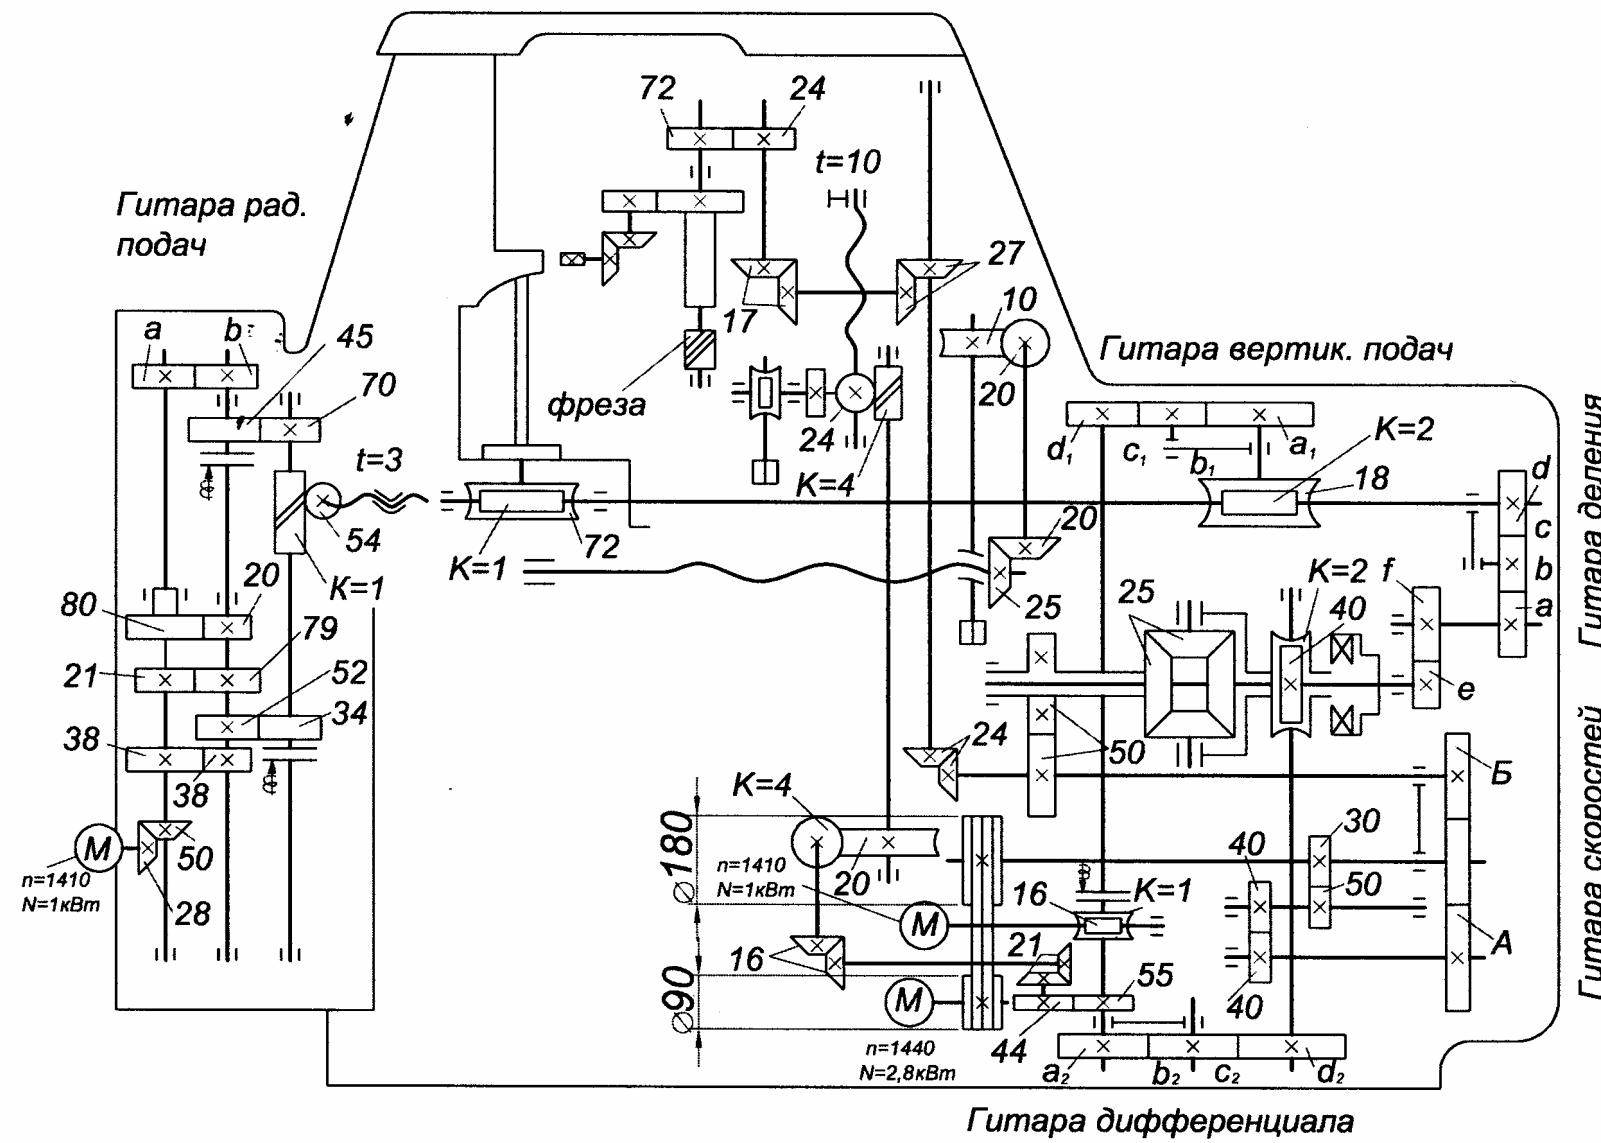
Кинематическая схема зубофрезерного станка мод. 5 В310
